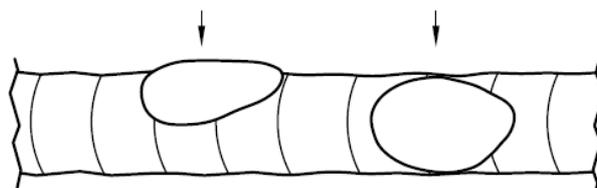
Perçage du cordon de soudure [CSMOFMI, les défauts de soudure]
